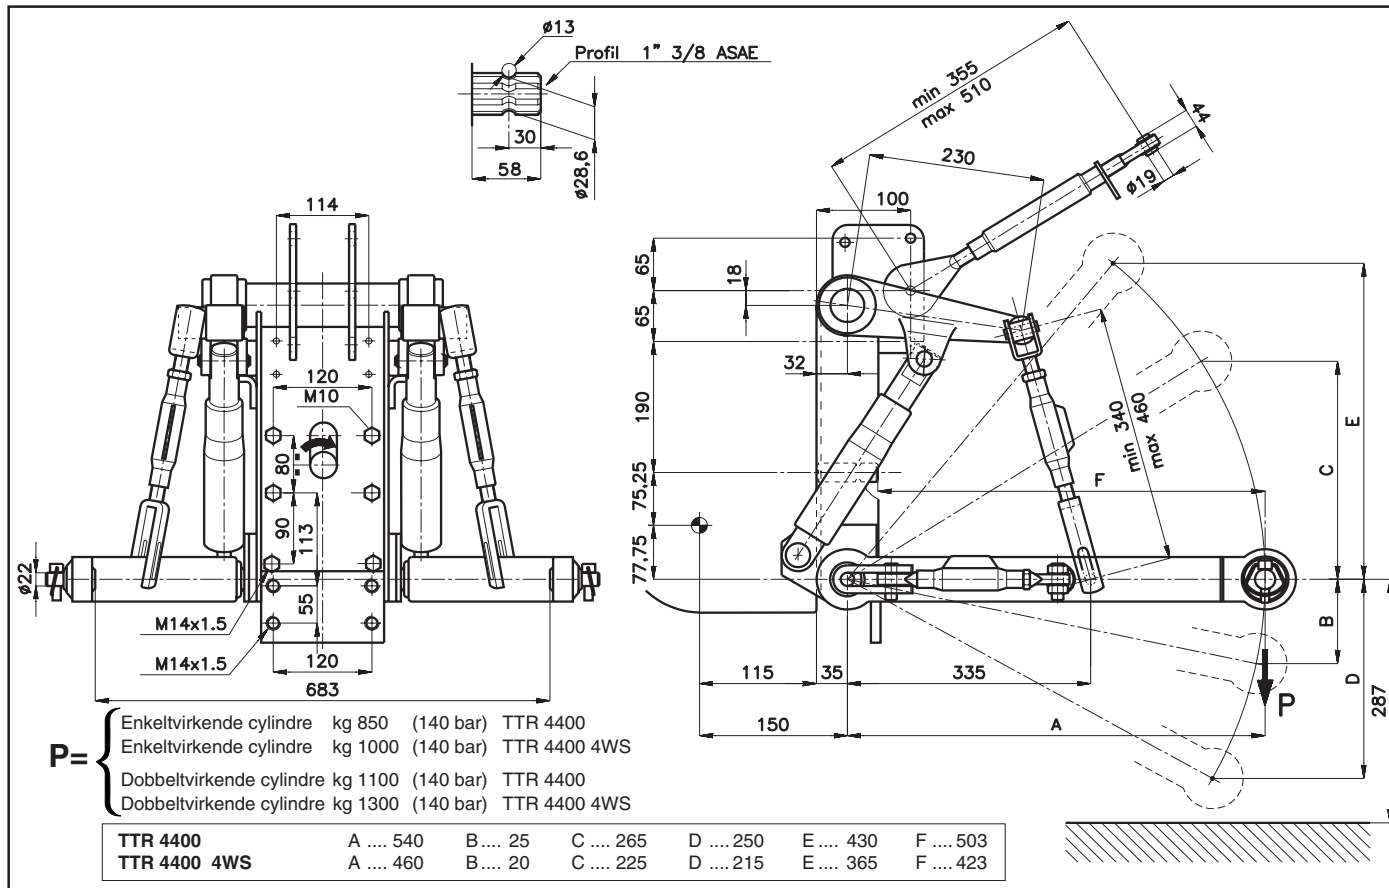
Dimensioner for trepunktskobling og flanger ved kraftudtag, med 6.50 - 16 hjul.
